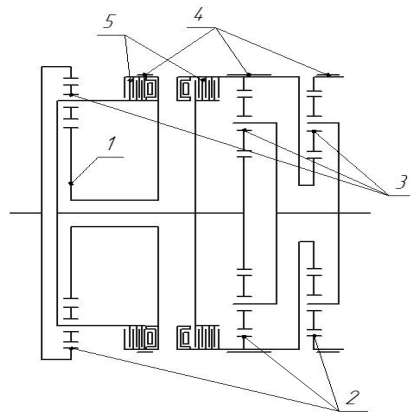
Кинематическая схема автоматической коробки переключения передач: 1-солнечная шестерня; 2-коронная шестерня; 3-сателлиты; 4- тормоз; 5- сцепление
